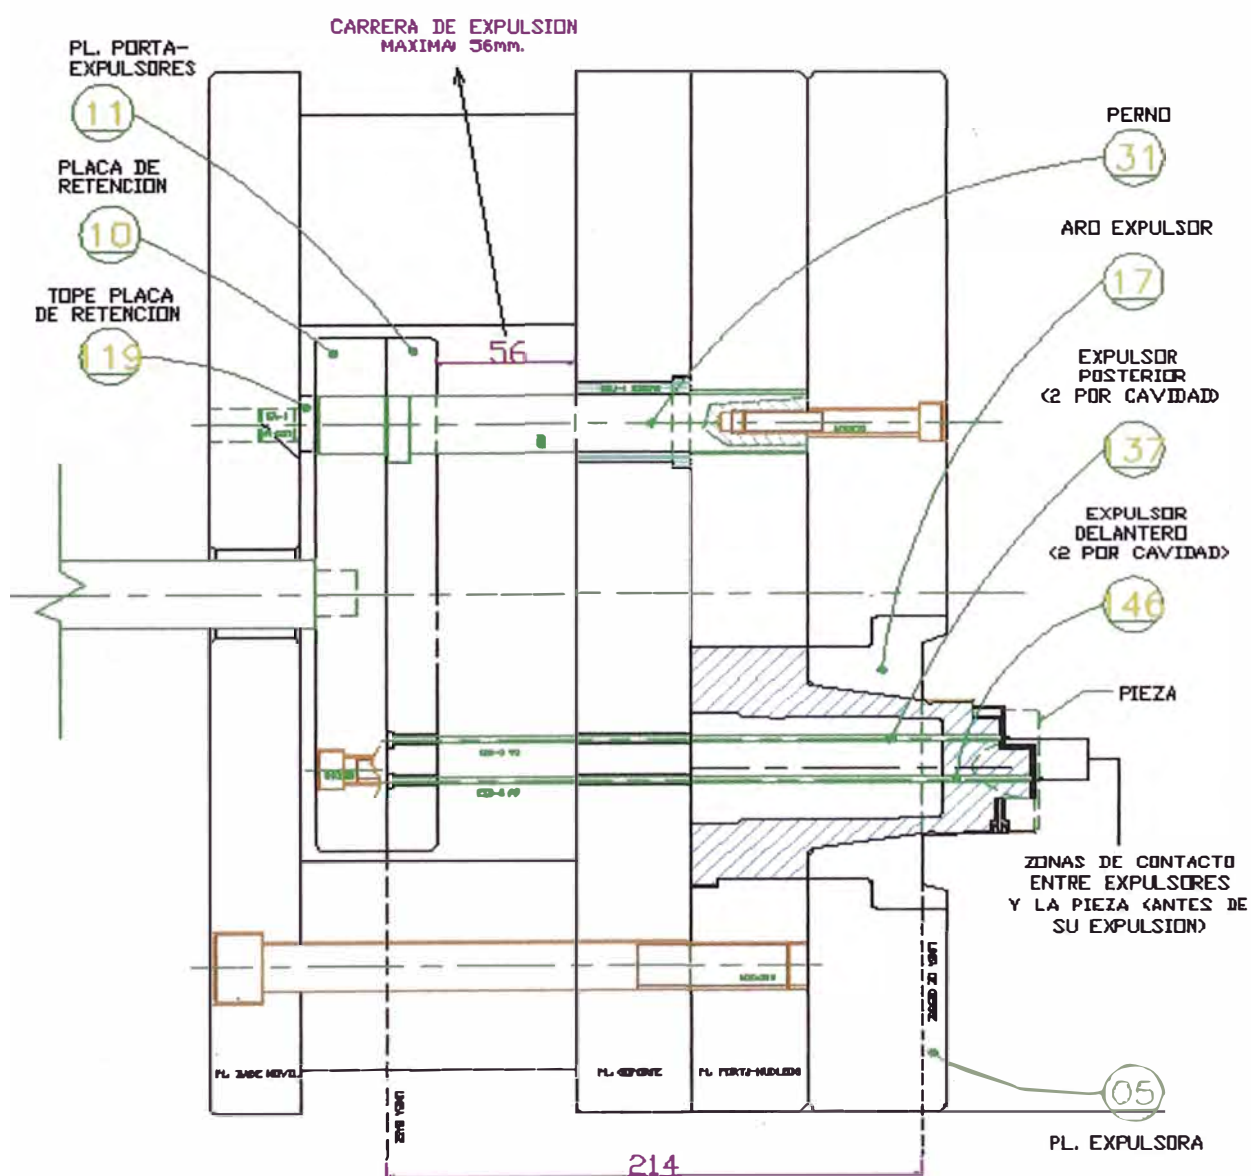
Sistema de expulsión del diseño base en posición de montaje.
